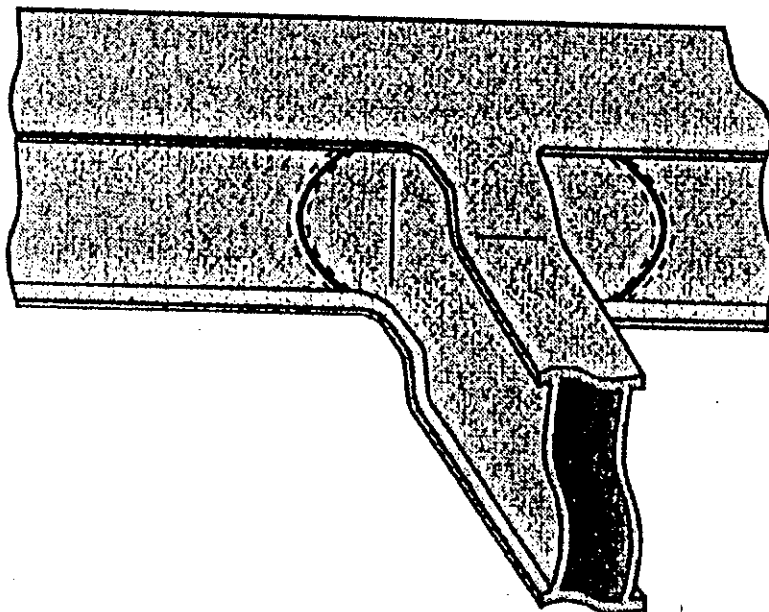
Контроль вертикальных сварных швов
